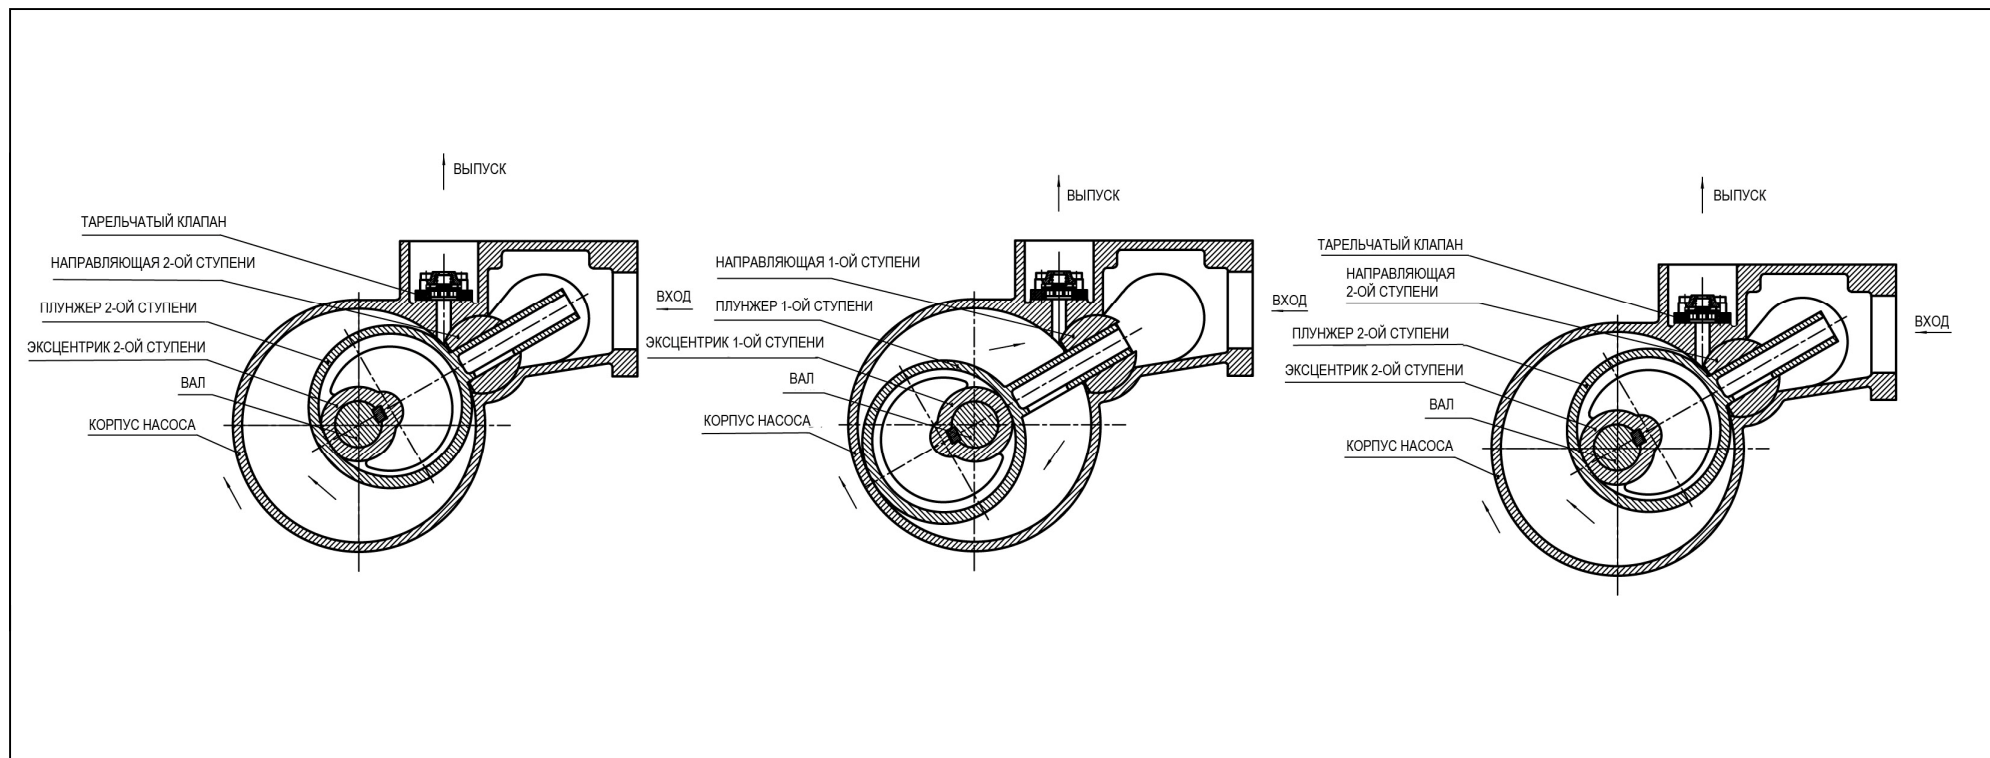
Одноступенчатый трехплунжерный агрегат. Схема работы
